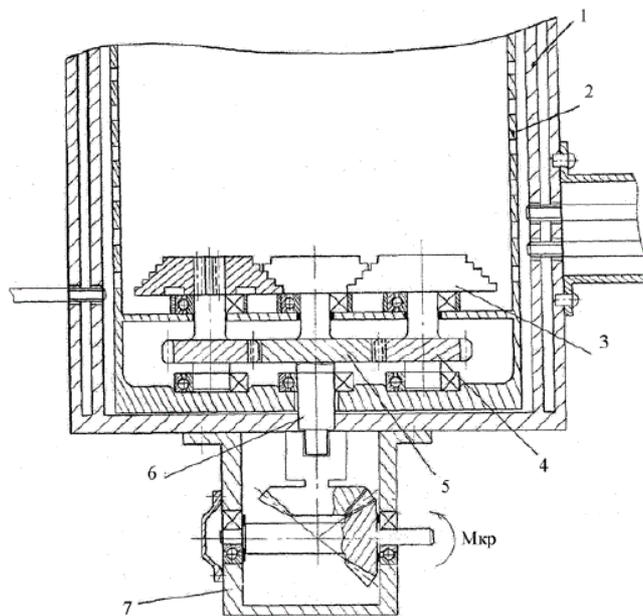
Установка для утилизации автомобильных шин 1 – экстрактор; 2 – перфорированная корзина; 3 – дисковые опоры; 4 – ведомые шестерни; 5 – ведущая шестерня; 6 – вал привода; 7 – конический редуктор
